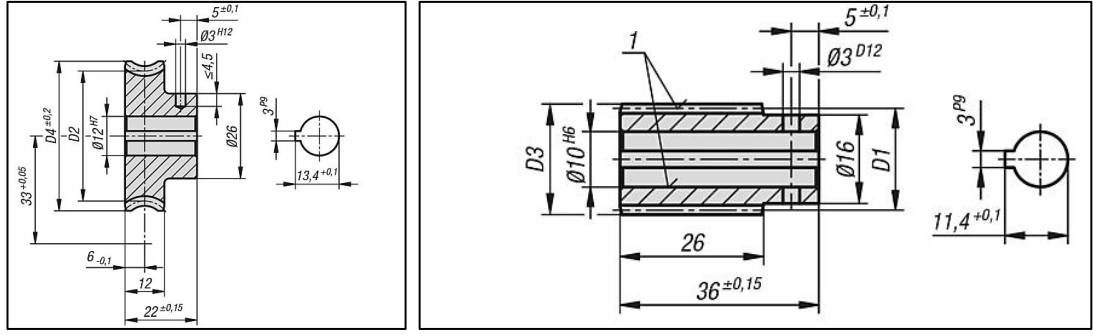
2. a) Sonsuz vida montaj mili, b) karşılık dişli montaj mili.
